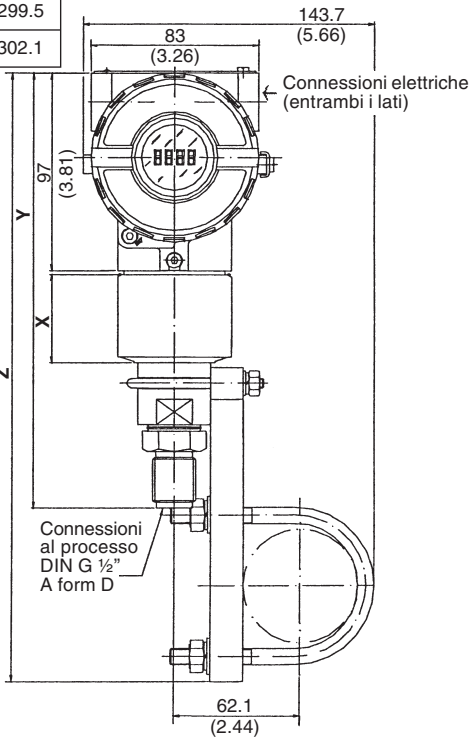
B - Dimensioni di ingombro e posizioni di montaggio per il trasmettitore LD290.
